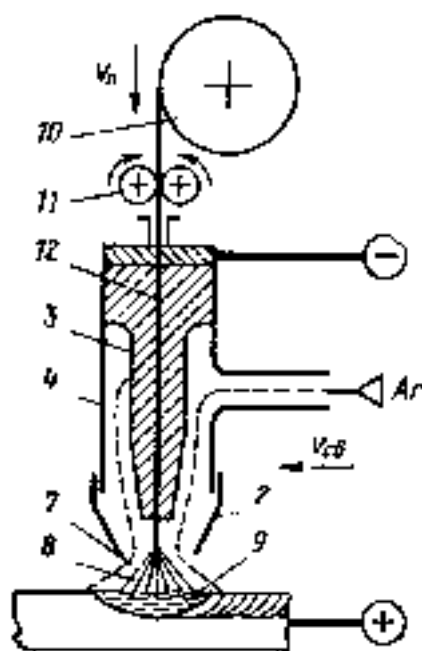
Схема аргонодуговой сварки алюминиевого сплава плавящимся электродом: 2 – сопло; 3 – токоподводящий мундштук; 4 – корпус горелки; 7 – атмосфера аргона; 8 – сварочная дуга; 9 – ванна расплавленного металла; 10 – кассета с проволокой; 11 – механизм подачи, 12 – плавящийся металлический электрод
